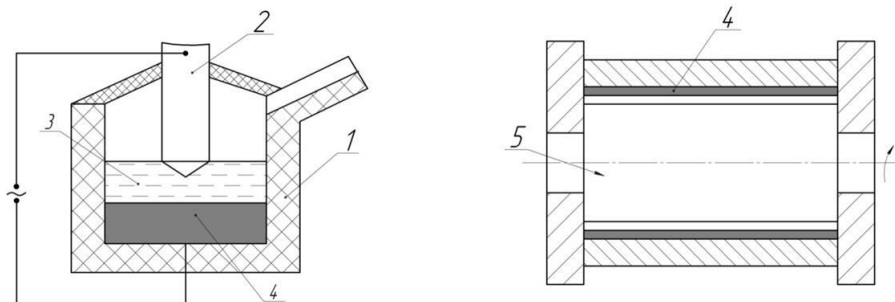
Схема електрошлакового тигельного плавлення із заливанням металу в обертову форму: 1 – тигель; 2 – електрод; 3 – шлак; 4 – розплав; 5 – заливання розплаву
